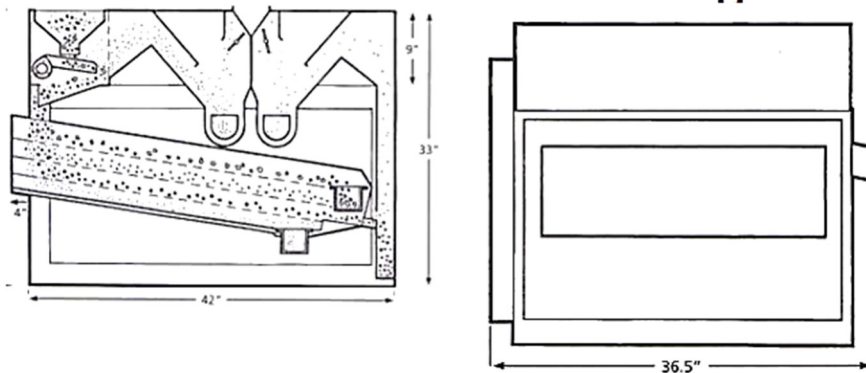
Віялка Bench Industries Mini Seed Cleaner
